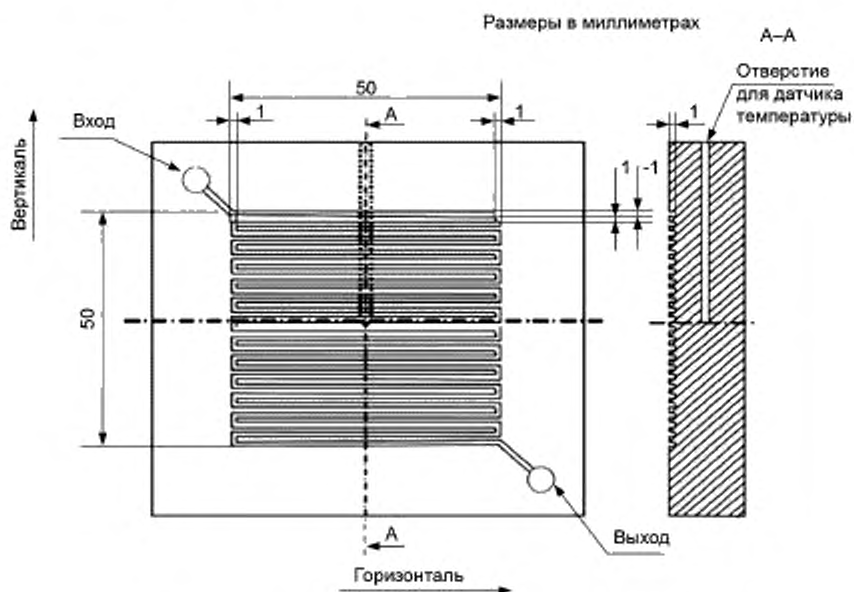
Конструкция газораспределительной пластины (одиночный извилистый канал)
